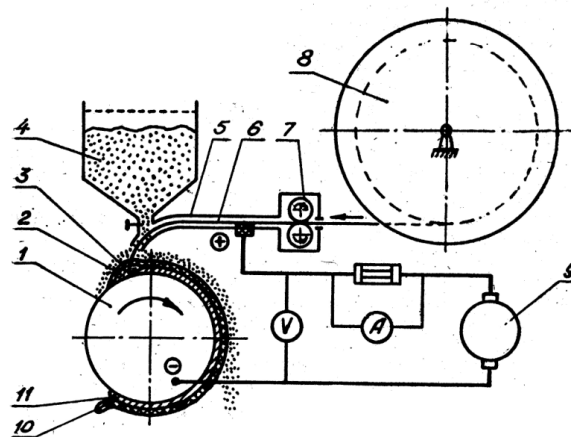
Схема автоматической наплавки под слоем флюса:
